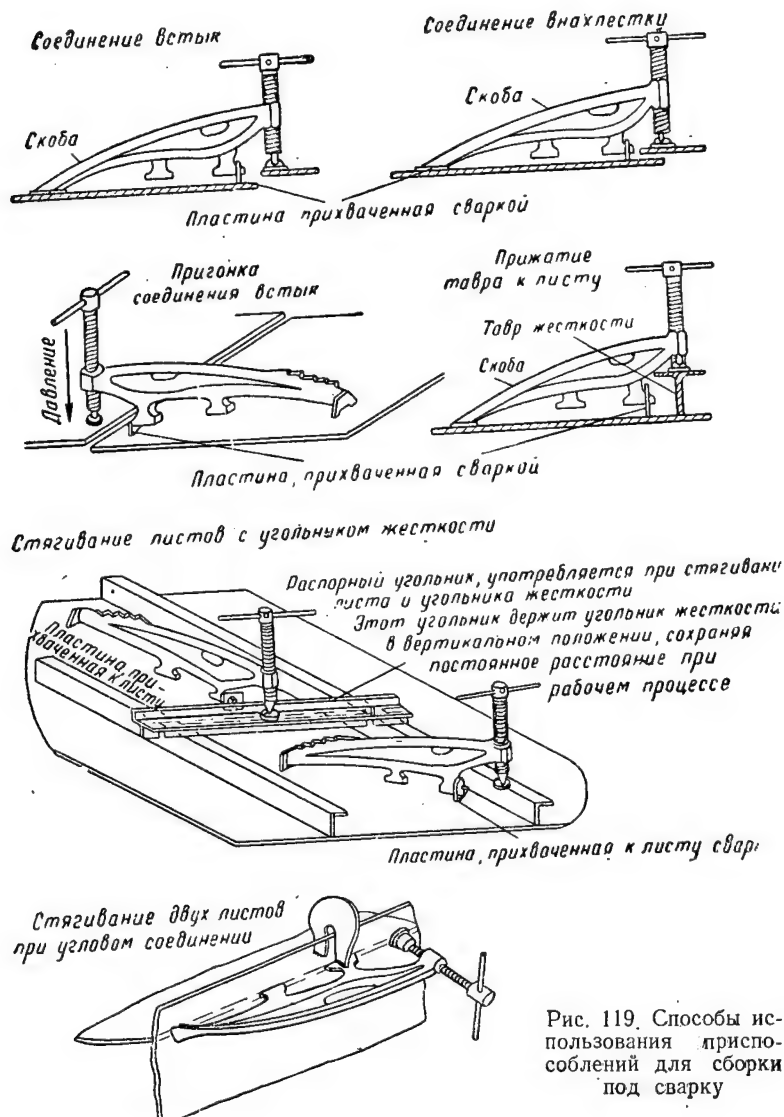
Способы использования приспособлений для сборки под сварку
